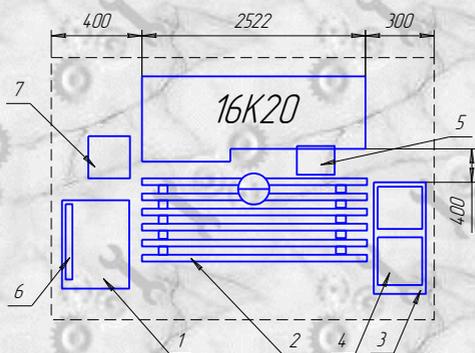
Пример планировки рабочего места токаря. 1 – инструментальный столик; 2 – решетка под ноги; 3 – приемный стол; 4 – тара с обрабатываемыми деталями; 5 – планшет для измерительного инструмента; 6 – подставка для чертежей; 7 – урна для мусора.
